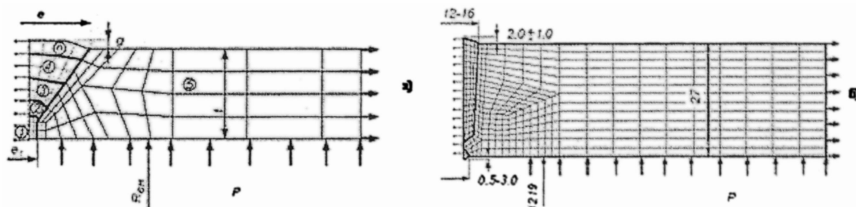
Фрагменты моделей сварных соединений: а – для V-образной разделки кромок (1...4, n – номера проходов; 5 – корпус трубы; P – внутреннее давление; $R_{вн}$ – внутренний радиус трубы; e, g – ширина и высота усиления); б – для щелевой разделки кромок
